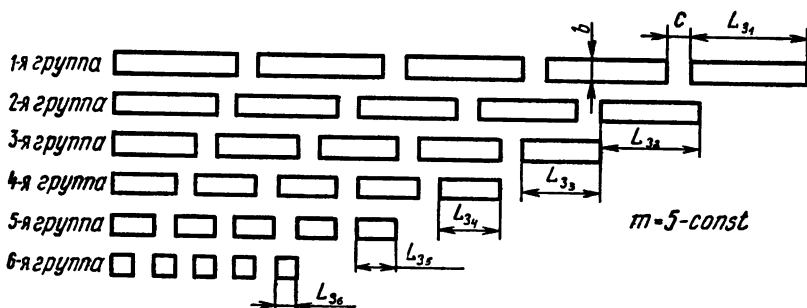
Заготовки, подвергаемые торцовому фрезерованию
